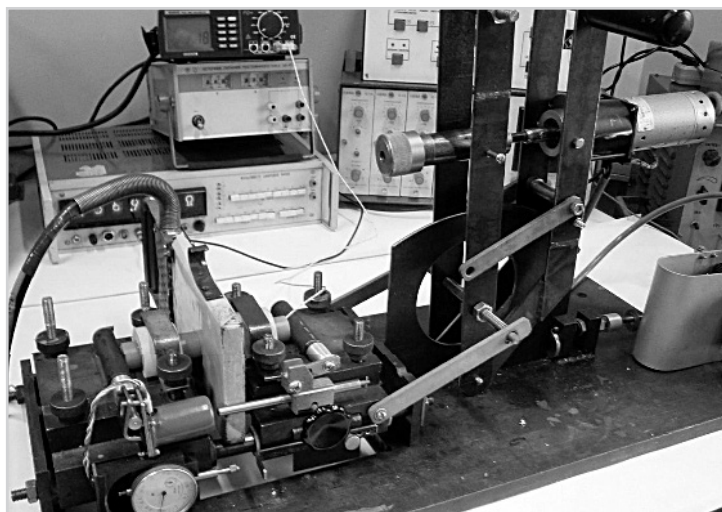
Экспериментальная установка для сварки термостойких пластмасс нагретым инструментом встык
